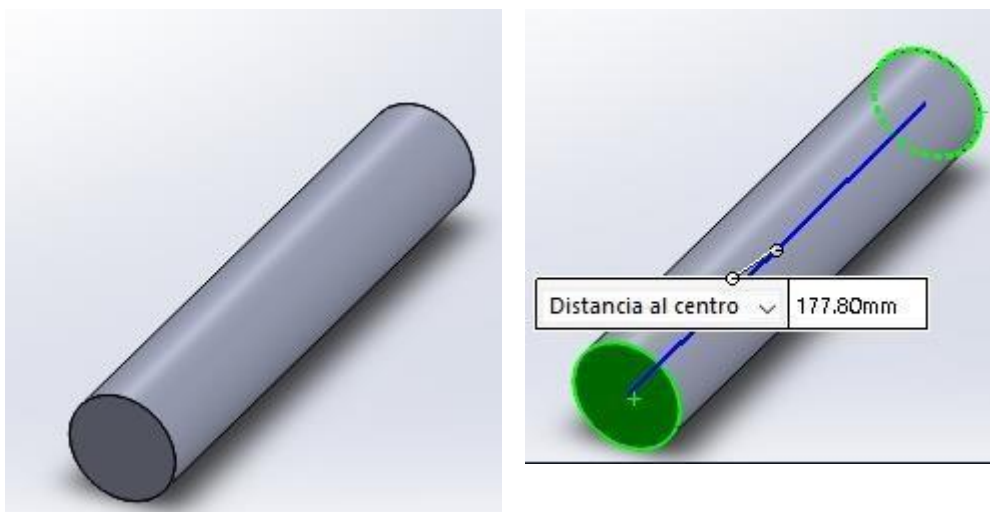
y 77: diseño y dimensiones del émbolo del pistón.
